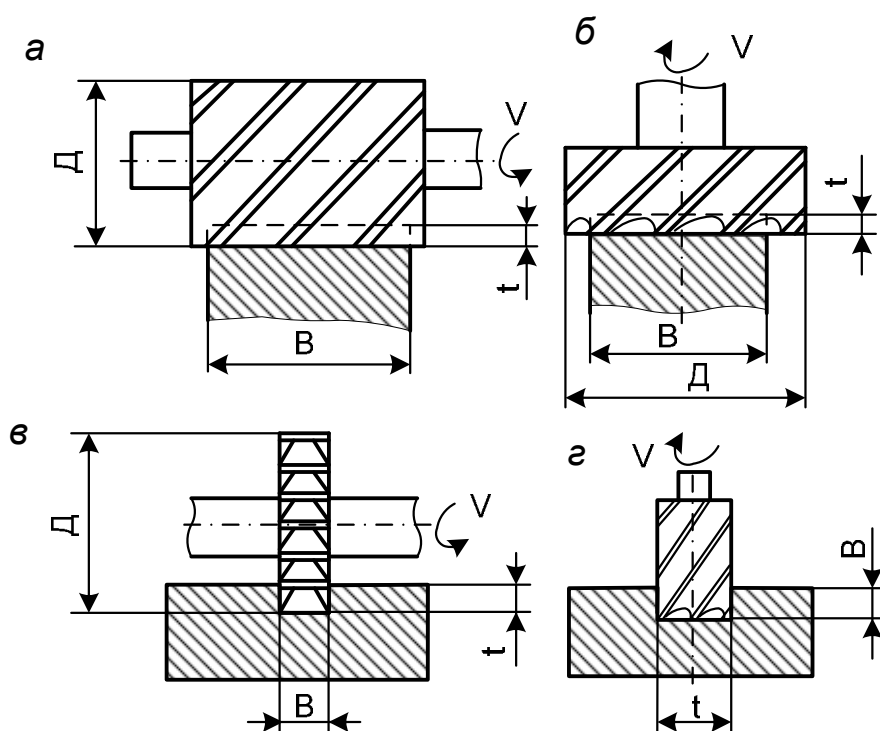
Виды фрезерования: а – фрезы цилиндрические; б – фрезы торцевые; в – фрезы дисковые; г – фрезы концевые
